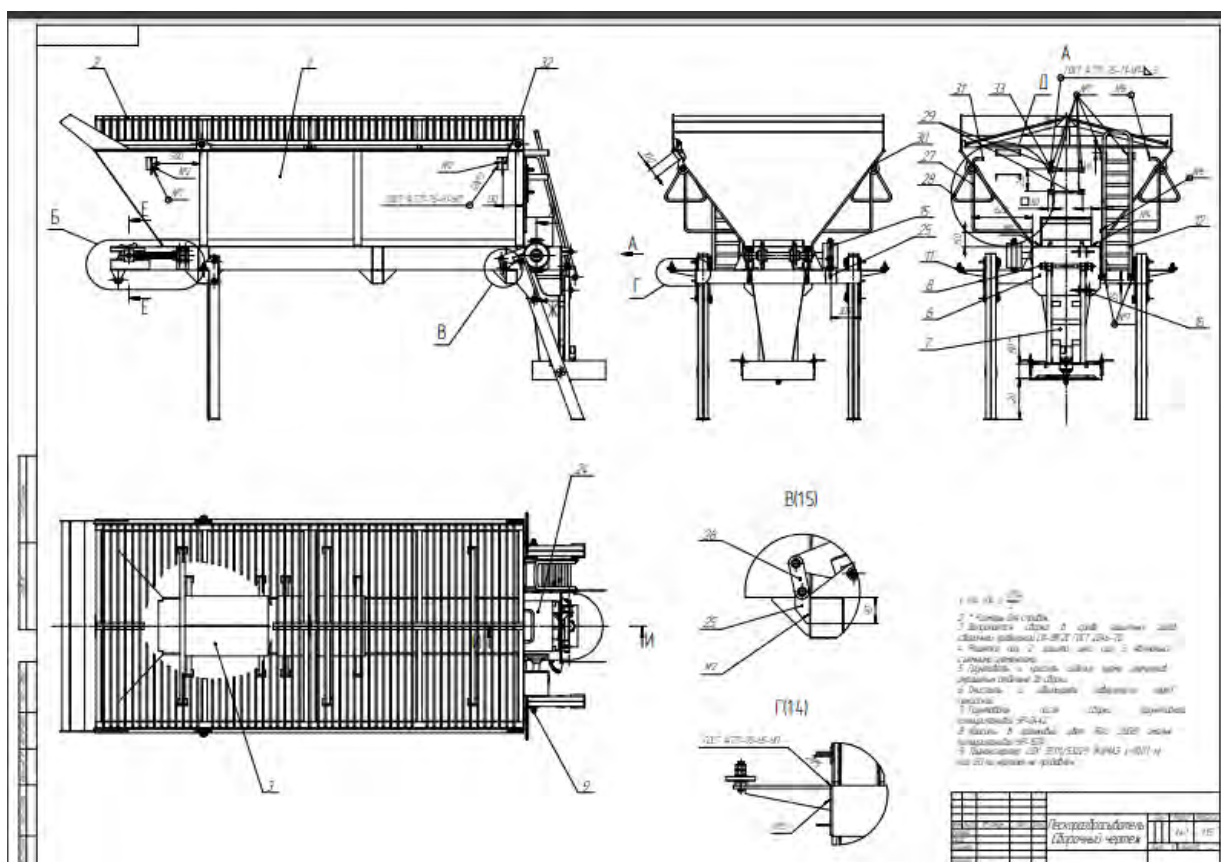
Сборочный чертеж бункера с пескоразбрасывателем
